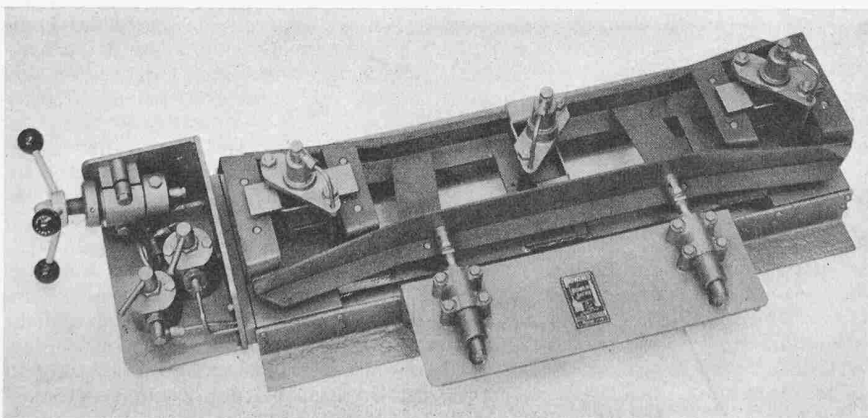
Durch Druckdosen zum Schweiessen festgehaltener Blechrahmen
